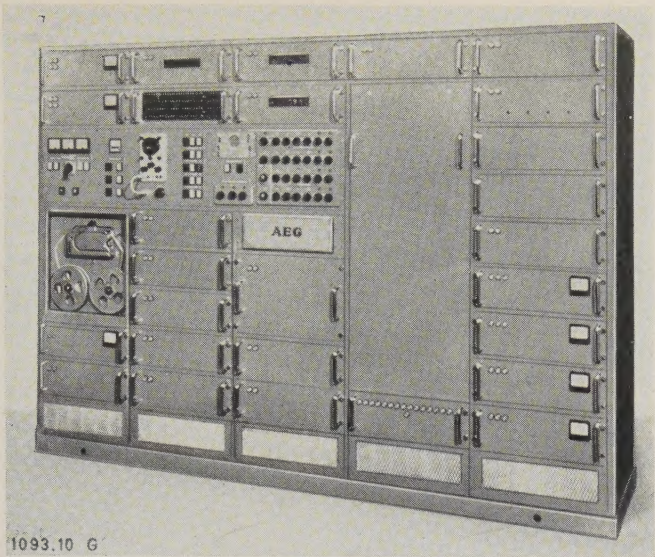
Numerische Steuerungseinrichtung für eine Großwerkzeugmaschine.
